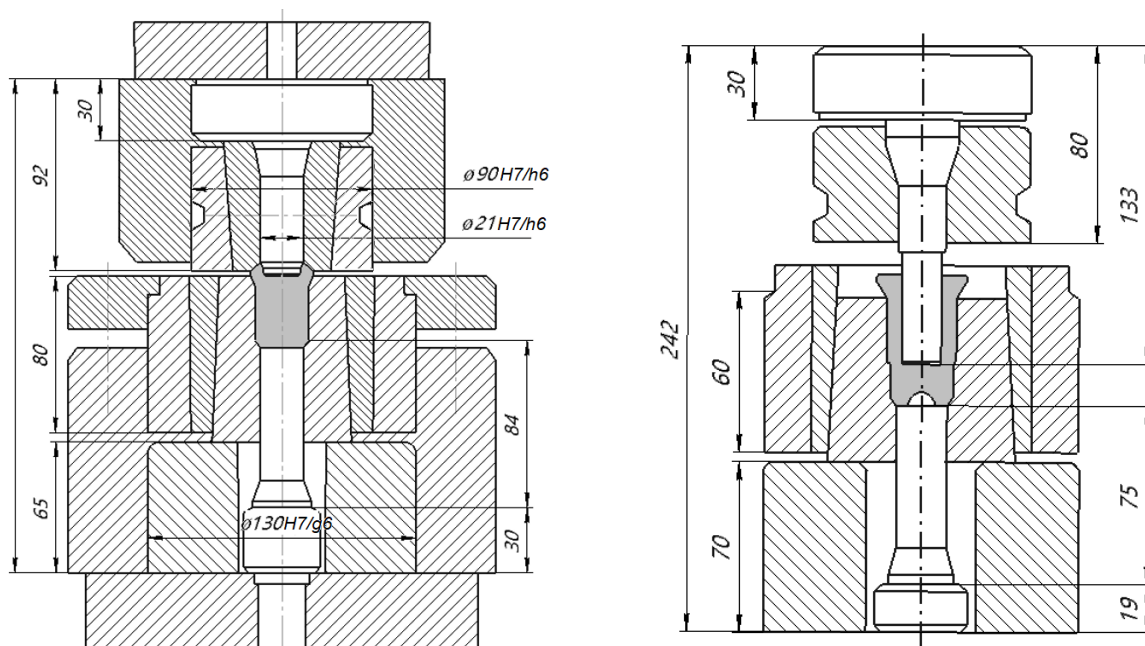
Змінні пакети для позицій № 1 і № 4 чотирьохпозиційного штампа для видавлювання ковпачкової гайки
